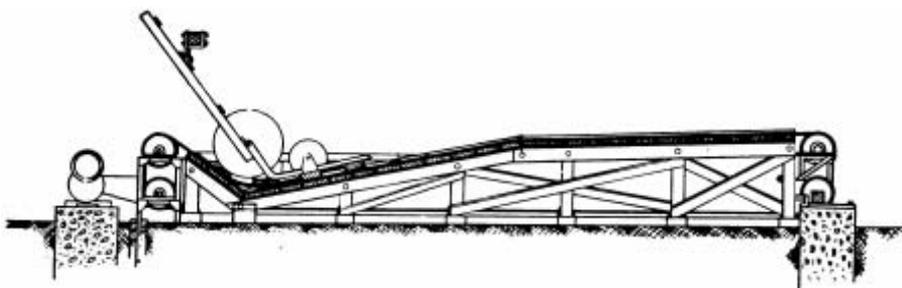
Tanque para imersão automática de madeira recém-serrada.
